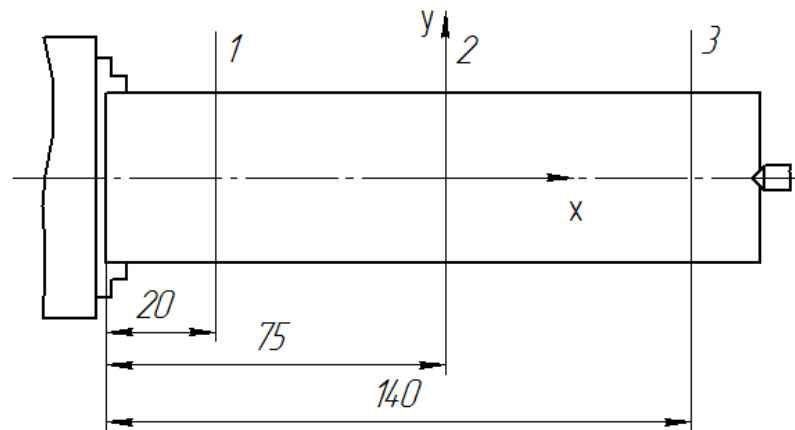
Розрахункова схема досліджуваної заготовки
